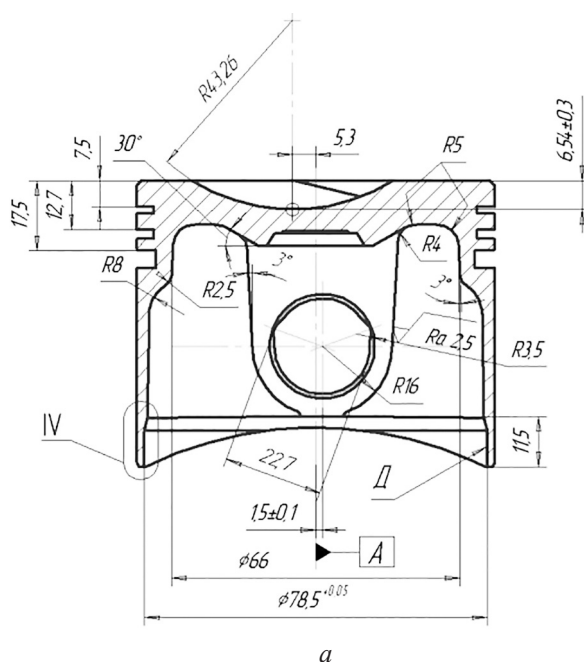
Поршень двигателя легкового автомобиля ВАЗ 21124:
